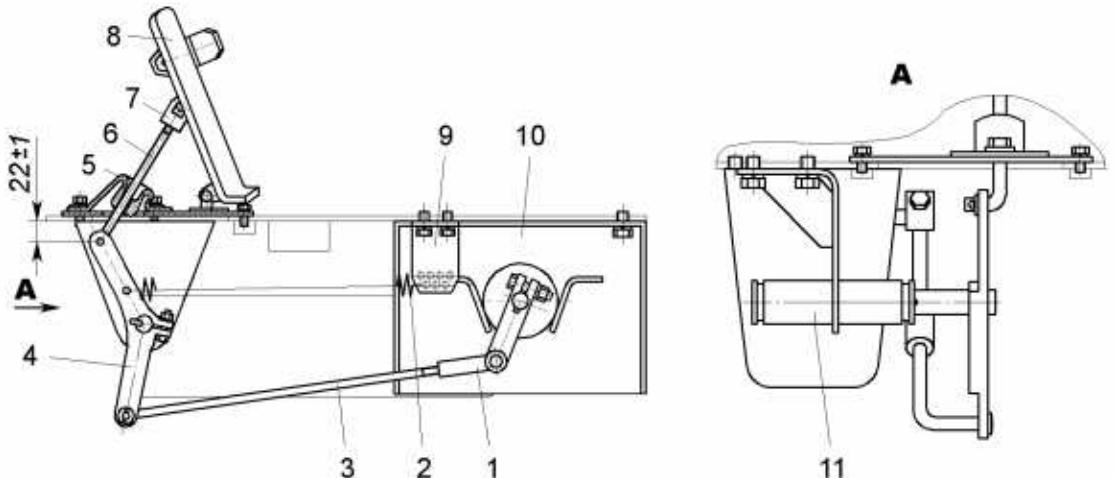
Установка ходового контроллера: 1 – вилка; 2 – пружина; 3, 6 – тяги; 4 – рычаг; 5 – защитный колпак; 7 – вилка; 8 – педаль ходовая; 9 – упор пружины; 10 – ходовой контроллер; 11 – вал акселератора
